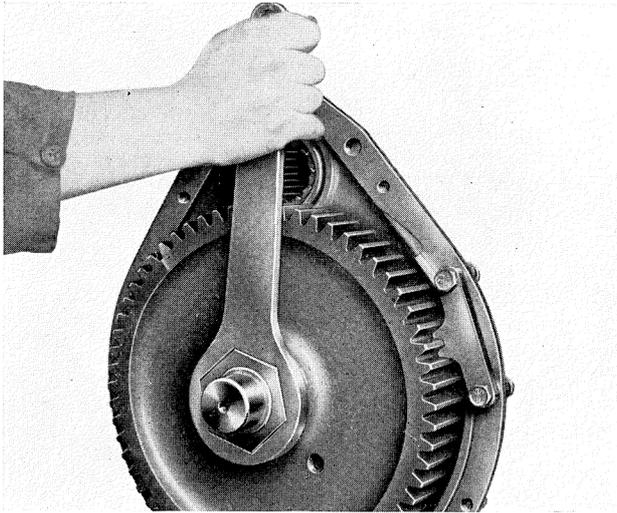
Démontage de l'écrou en bout de l'arbre de roue motrice.
